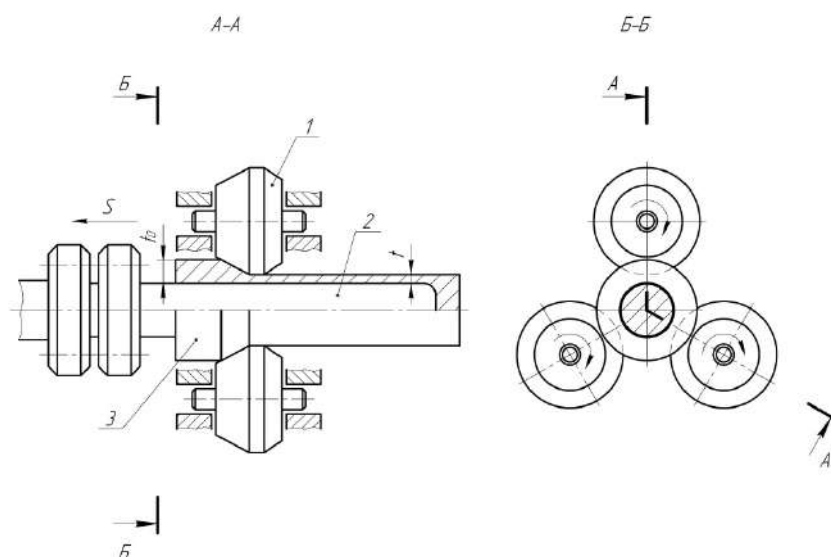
Схема трехроликковой раскатки корпусов головных и хвостовых труб: 1 - ролики; 2 - оправка; 3 – корпус трубы [72]
